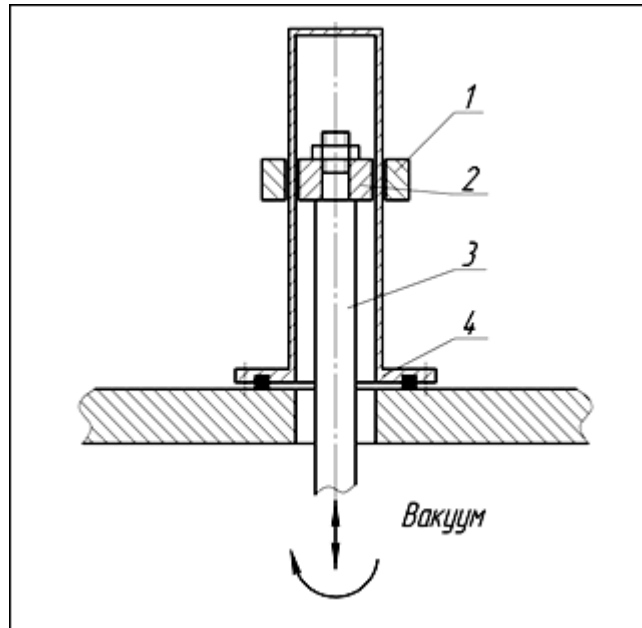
Бесконтактный ввод движения в вакуум с постоянными магнитами радиального типа:
